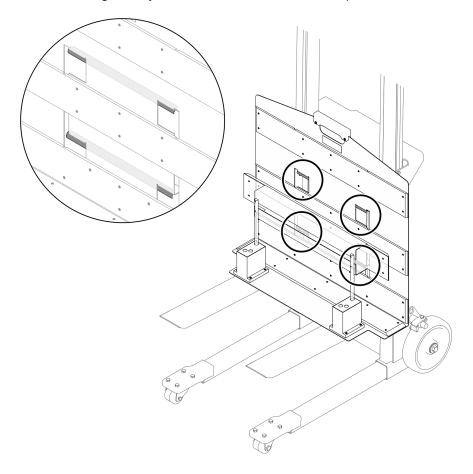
Instalación adecuada del accesorio de la herramienta de elevación
